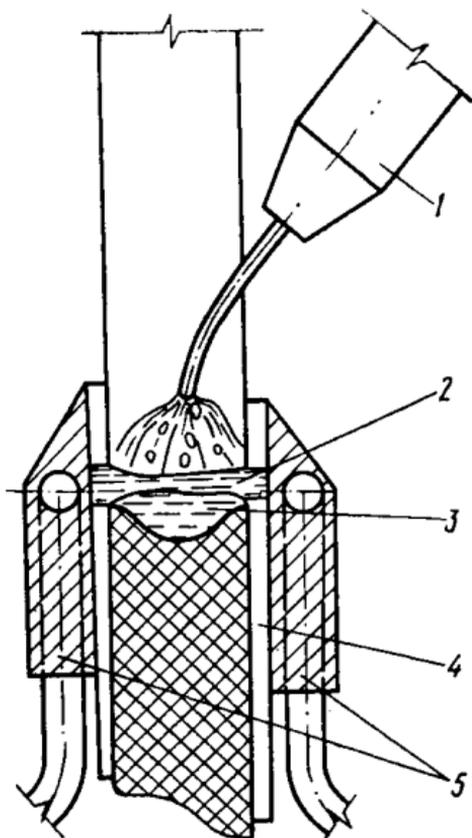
Схема формирования шва при сварке на вертикальной плоскости аппаратом А-1150У:
